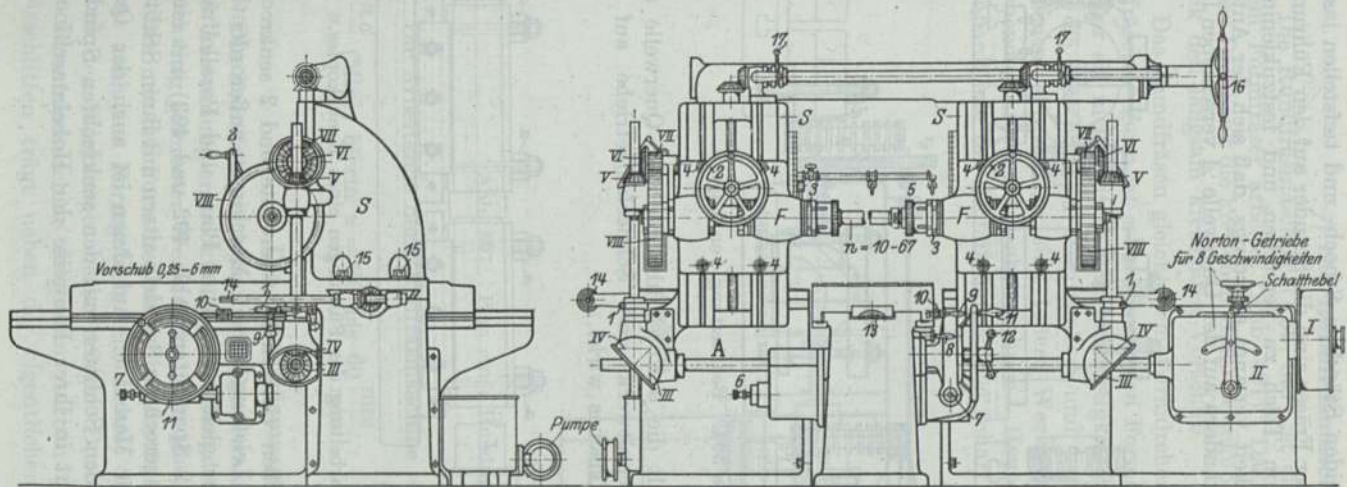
und 586. Langfräsmaschine. Gildemeister & Co., A.-G., Bielefeld.
